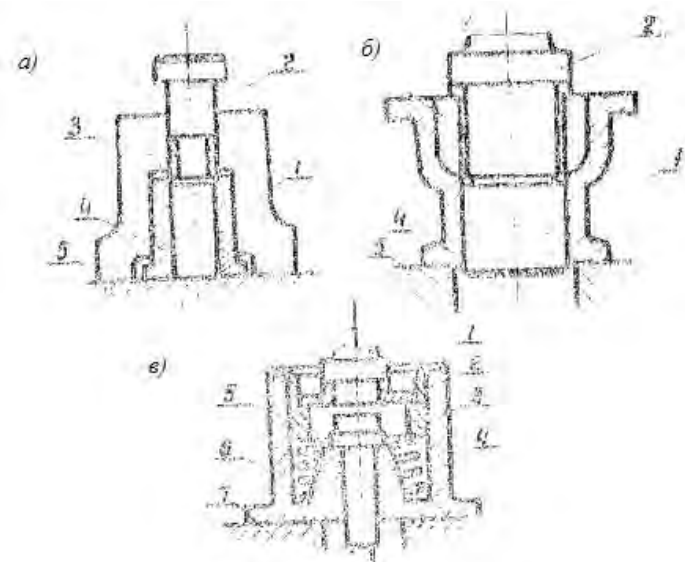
Схемы приспособлений к универсальным прессам.
